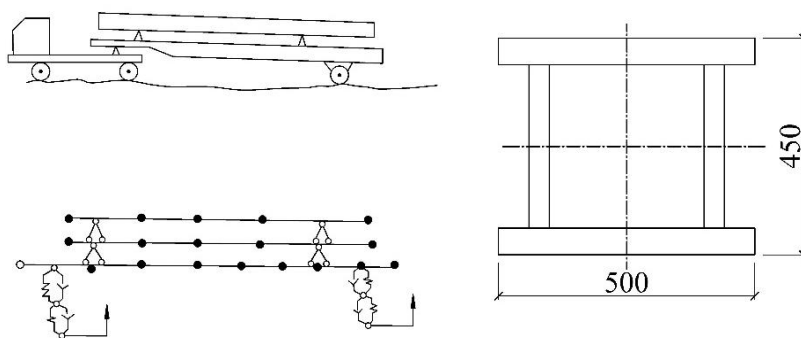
Общий вид, расчетная схема прицепа и поперечное сечение продольной несущей балки
